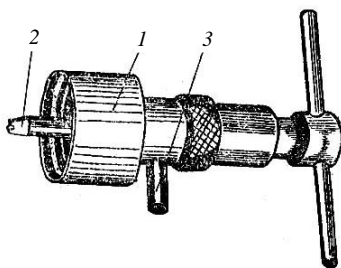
Приспособление для регулировки гильзы золотника распределителя: 1 – накидная гайка; 2 – отвертка для регулировки; 3 – патрубок стока масла
